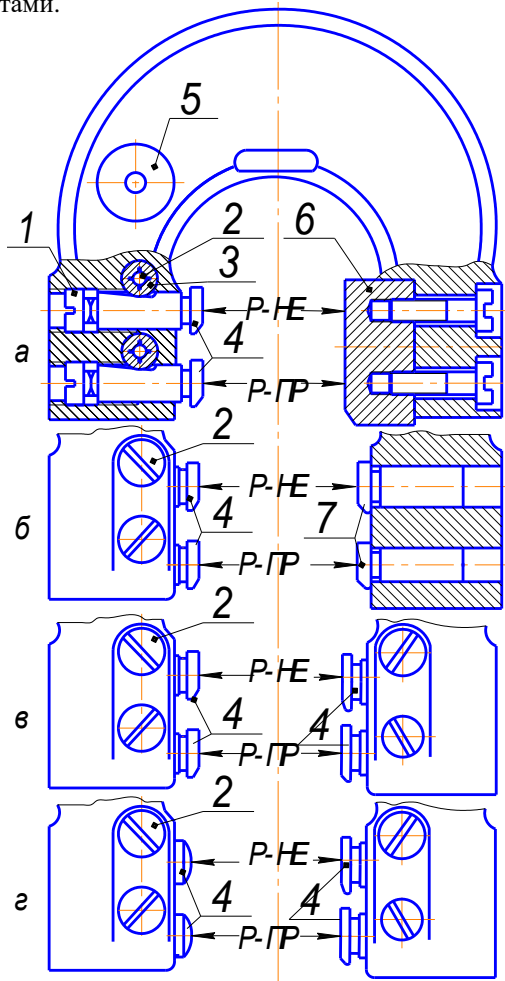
Односторонний двупредельный калибр - скоба для контроля вала $\varnothing 55h7$
